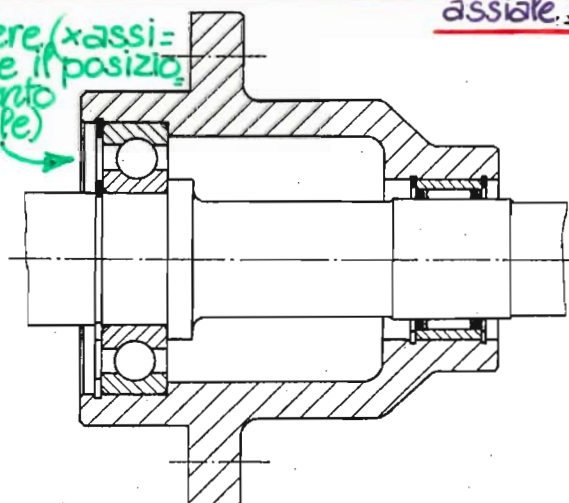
Montaggio di un cuscinetto a rullini senza anello interno e di un cuscinetto radiale rigido a sfere che assicura il posizionamento assiale.
